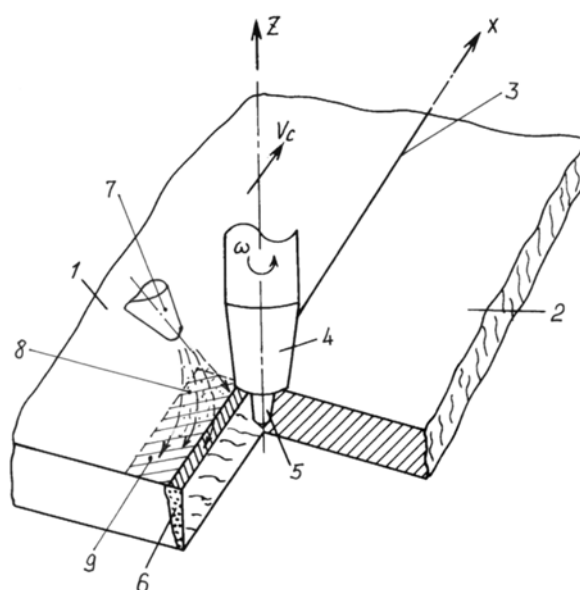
Схема СТП алюминиевых сплавов с охлаждением металла шва направленными воздушно-водяными струями:
